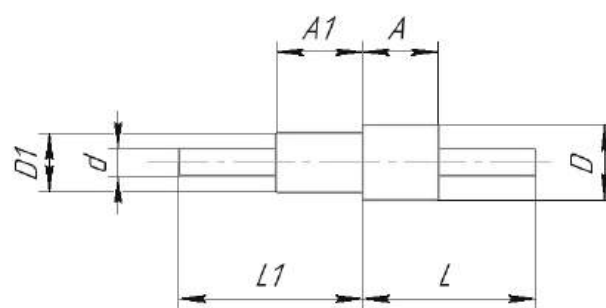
Габаритные размеры фильтров Ф26, типоразмер 7
